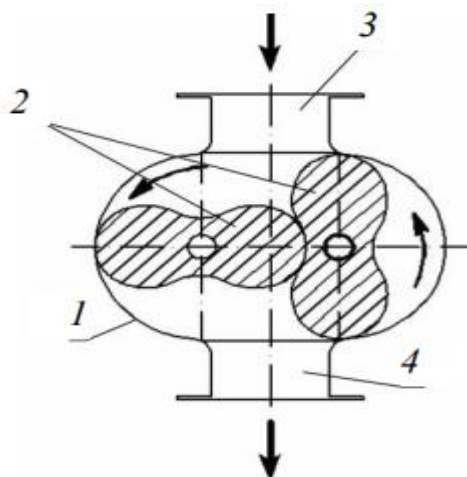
Ротаційний компресор газодувка) з дволопатевиими роторами
